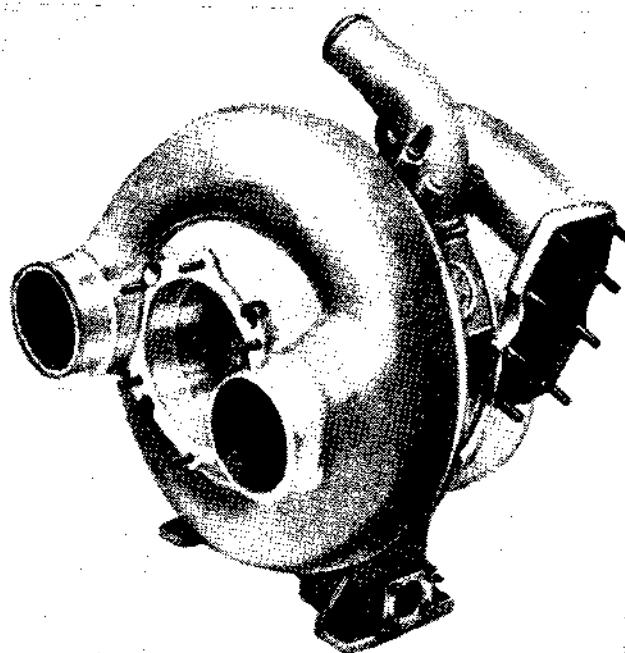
Схема взаимных положений корпусов турбокомпрессора ТКР-14Н (вид со стороны компрессора)
